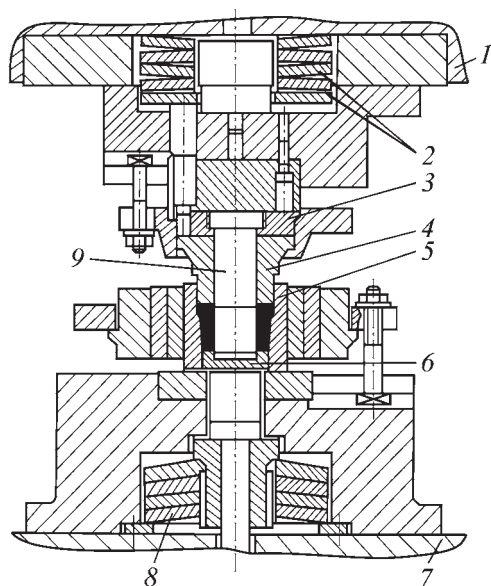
Штамп для закрытой полугорячей штамповки поковок внутренних колец конических роликовых подшипников:
